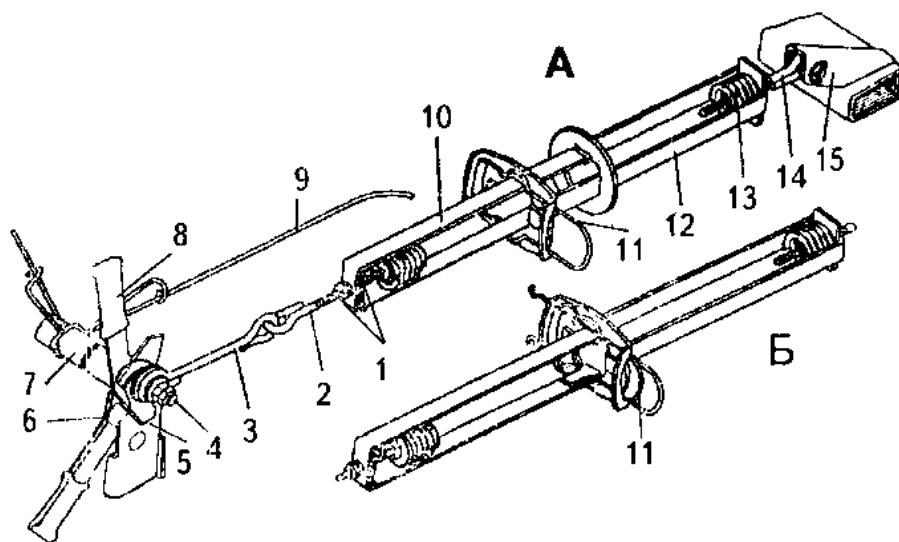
Устройство уравнивающее: а – установка уравнивающего устройства; б – транспортное положение фиксатора (рабочее его положение изображено штрихпунктирными линиями): 1 – гайка регулировочная; 2 – растяжка; 3 – шпиргель; 4 – цапфа эксцентрическая; 5 – стойка; 6 – упор; 7 – балка нормализатора; 8 – рычаг; 9 – палец; 10, 12 – обойма; 11 – фиксатор; 13 – пружина растяжения; 14 – растяжка; 15 – балка платформы
